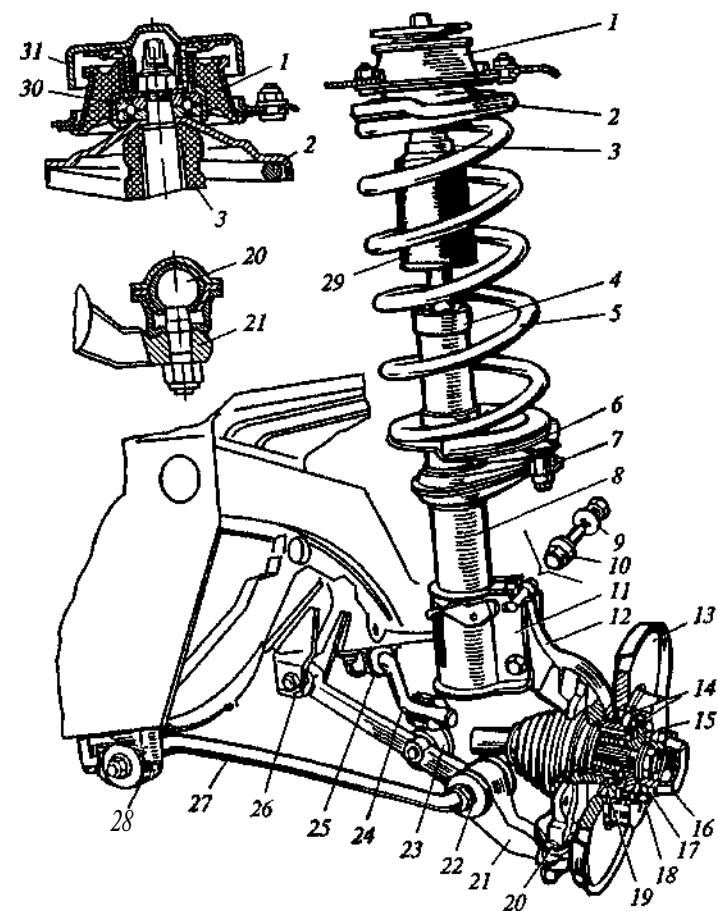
Передняя подвеска переднеприводного легкового автомобиля ВАЗ. 1, 2, 4, 6 и 25 — опоры, 3 — буфер; 5 — пружина, 7 и 21 — рычаги; 8 и 23 — стойки; 9 — шайба, 10 — регулировочный болт; 11, 26 и 28 — кронштейны; 12 — кулак; 13 — тормозной диск, 14 — кольцо; 15 — ступица; 16 и 31 — колпаки; 17 — хвостовик; 18 — штифт; 19 и 30 — подшипники; 20 — шарнир, 22 — регулировочные шайбы; 24 — стабилизатор; 27 — растяжка; 29 — кожух
